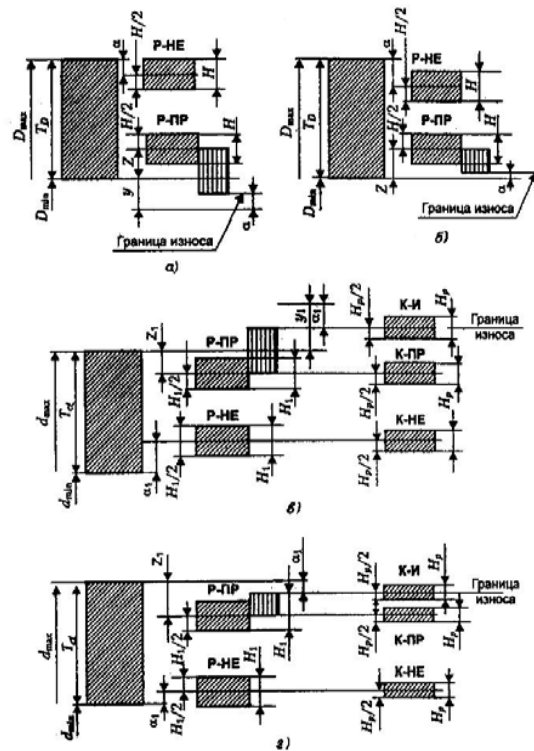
Схемы расположения допусков калибров для Номинальных размеров св. 180 до 500 мм:
